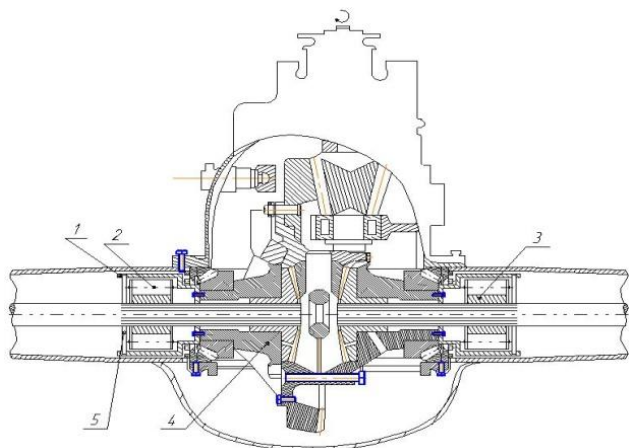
Принципиальная схема автоматической блокировки дифференциала: 1 – наружная обойма; 2 – сепаратор с роликами и пружинами; 3 – звездочка; 4 – корпус дифференциала; 5 – стопорное кольцо
